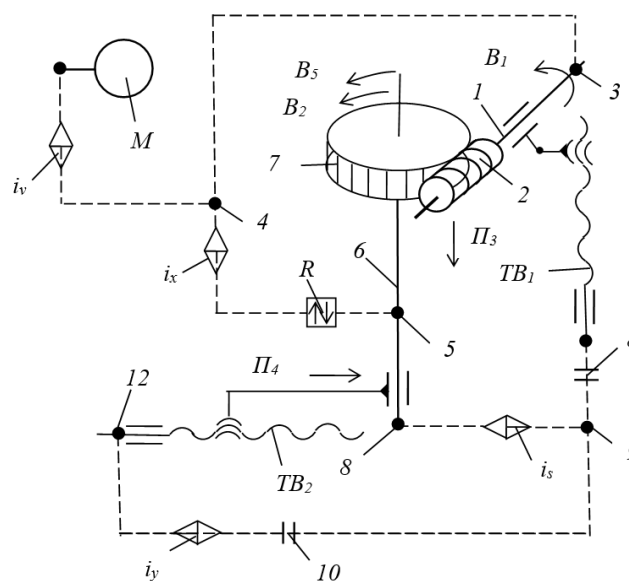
Структурная схема зубофрезерного станка для обработки цилиндрических колес
